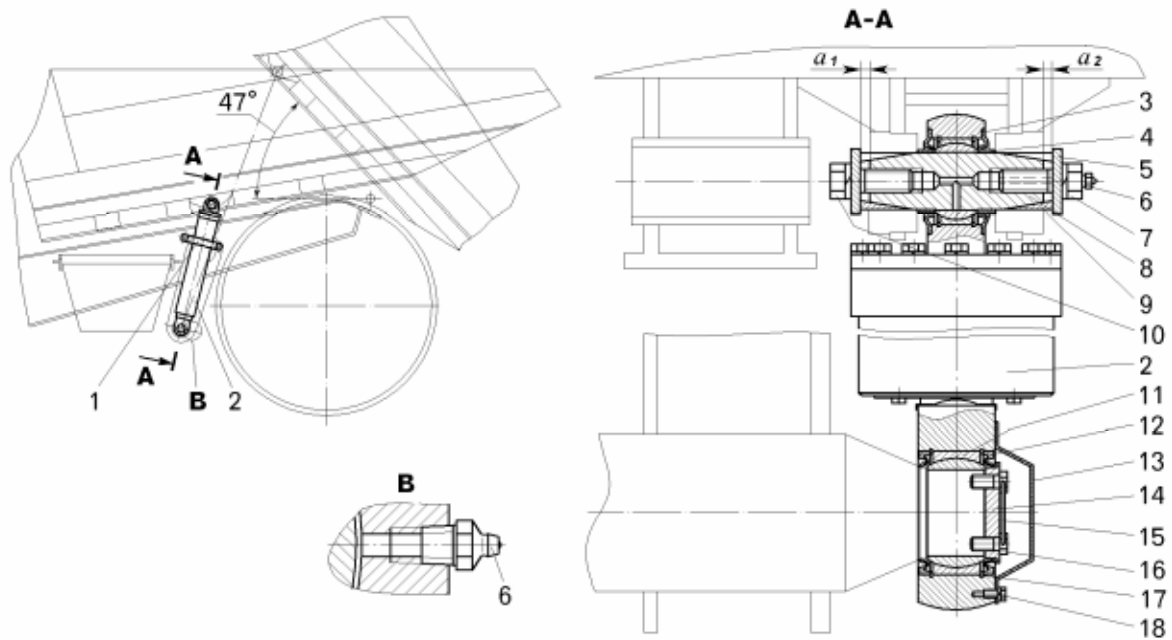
Установка цилиндров опрокидывающего механизма:
